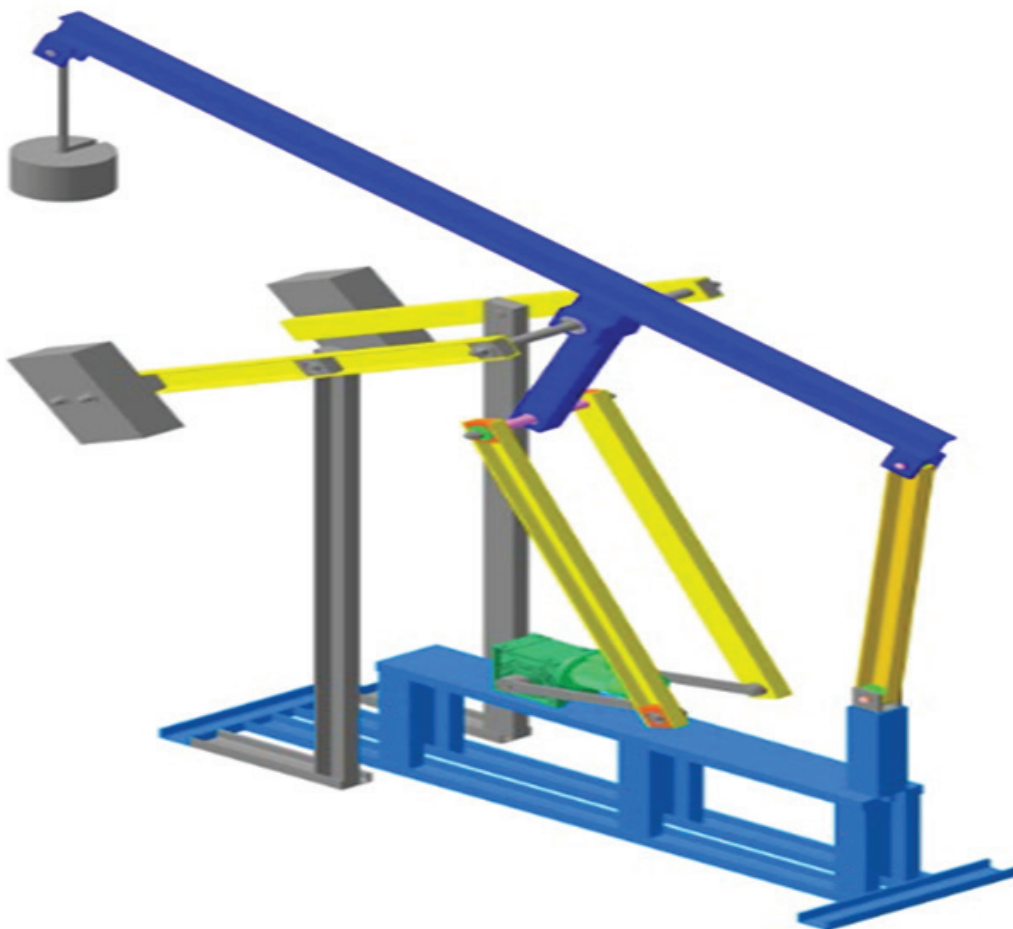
3Д схема механизма привода штанговых насосных установок в верхнем положении
